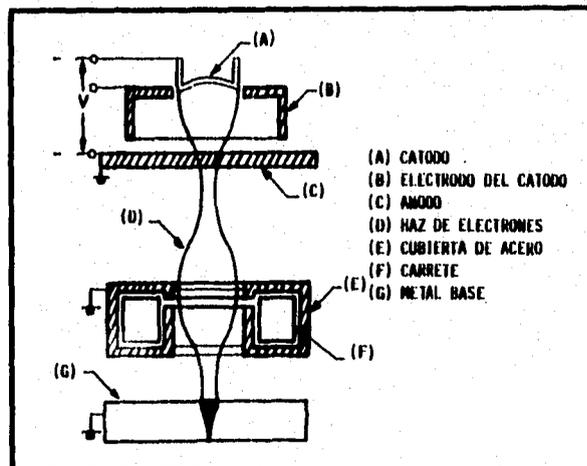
DETALLE DEL PROCESO DE SOLDADURA EBW.
